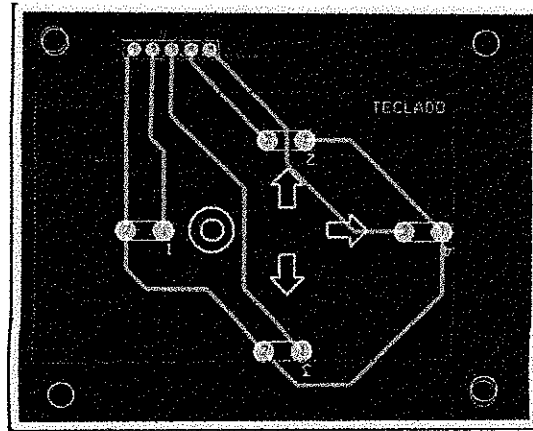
TECLADO MATRICIAL IMPRESO ORCAD LAYOUT
